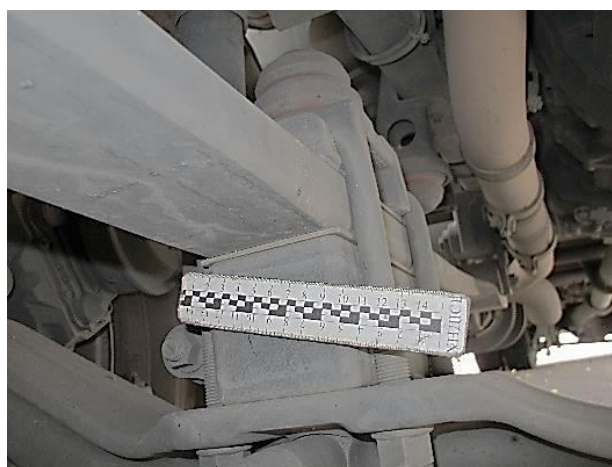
Детальний вигляд кріплення ресори підвіски правого переднього колеса автомобіля MAN TGM до правої частини балки передньої підвіски
